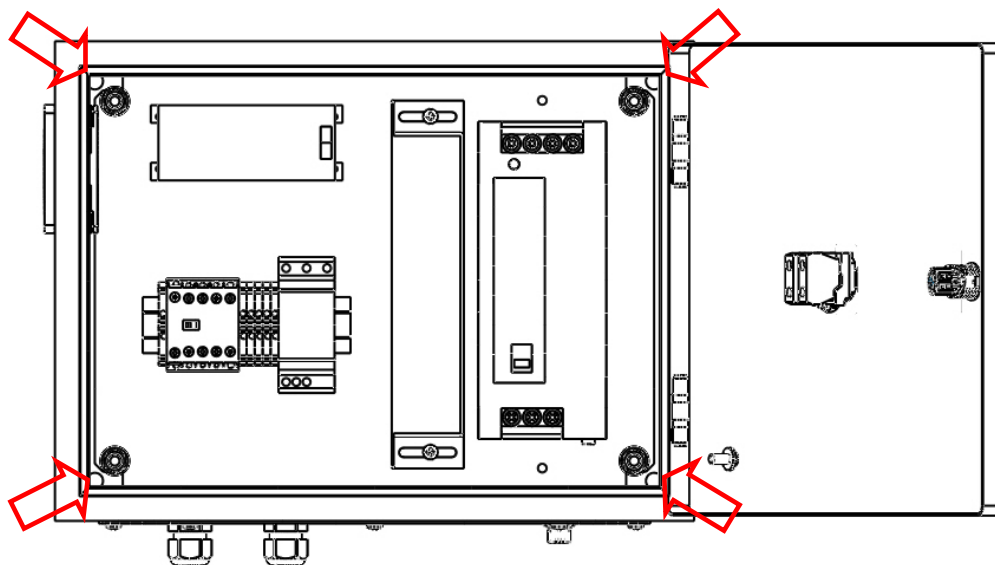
Anclaje del armario de maniobra en fijación mural.
